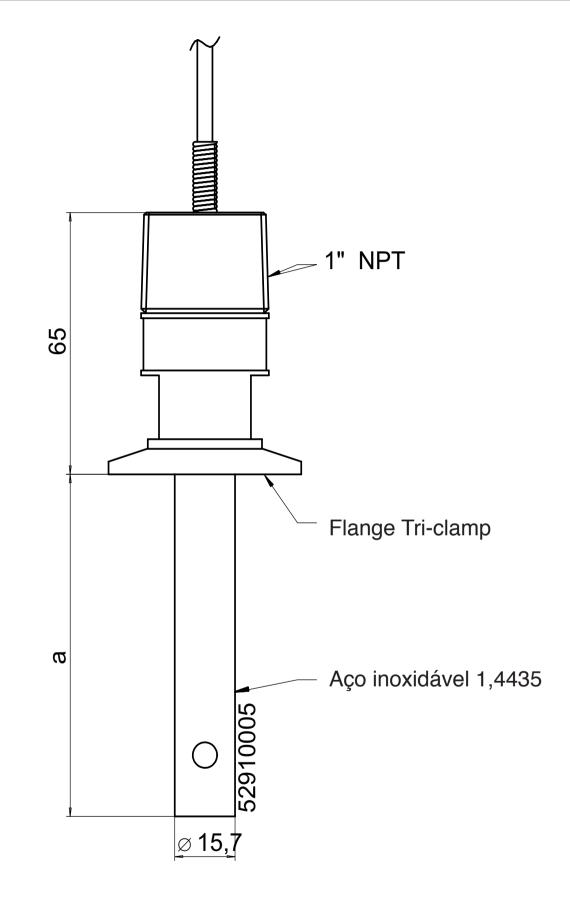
Desenho das dimensões do InPro®7001 com 2 eletrodos
